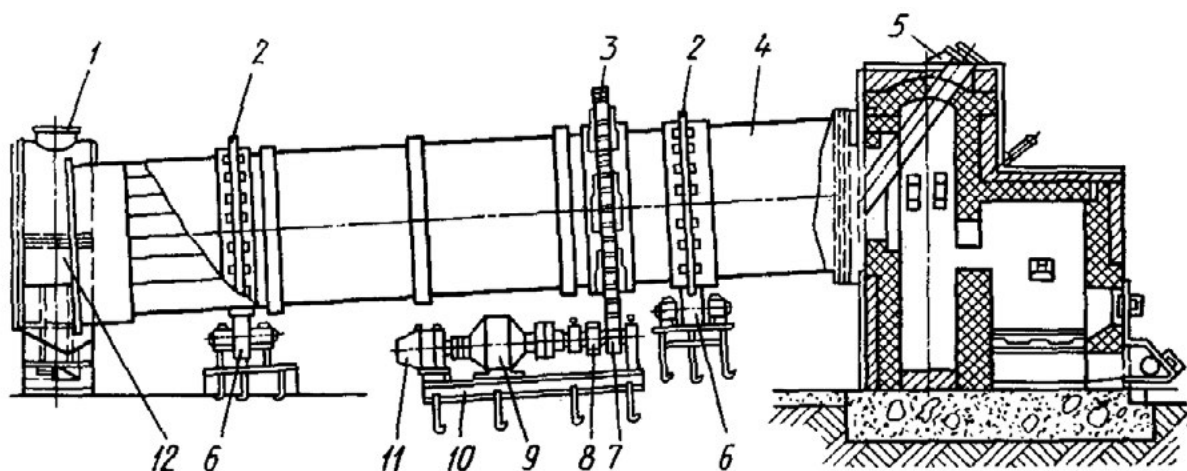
Вращающаяся печь: 1 – патрубок; 2 – бандаж; 3 – венцовая шестерня; 4 – сварной стальной цилиндр; 5 – загрузочная течка; 6 – опорный ролик; 7 – подвенцовая шестерня; 8 – зубчатая пара; 9 – редуктор; 10 – сварная плита; 11 – электродвигатель; 12 – разгрузочная камера
